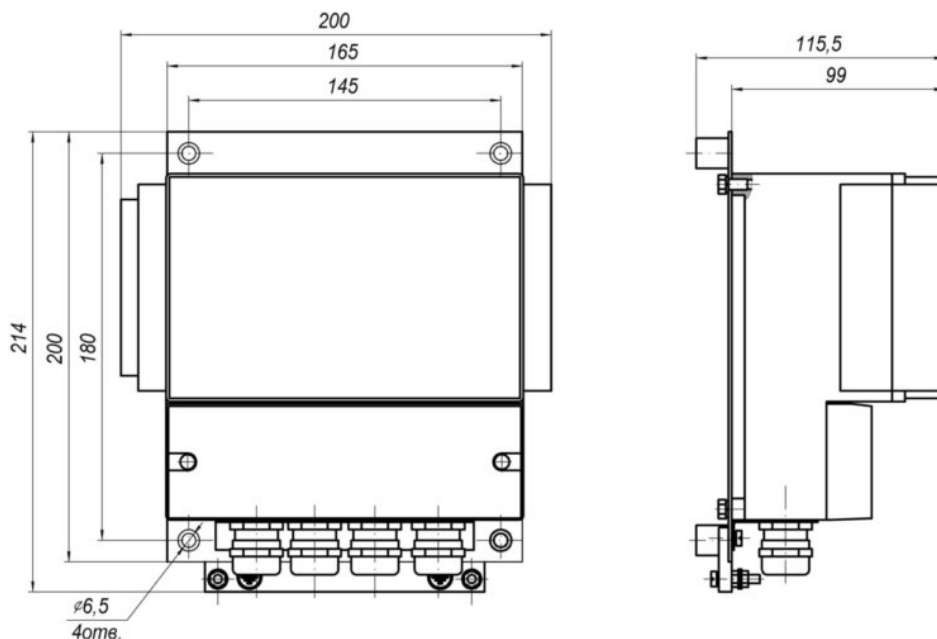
Габаритные размеры измерительного прибора АЖК-3122.х.АС
